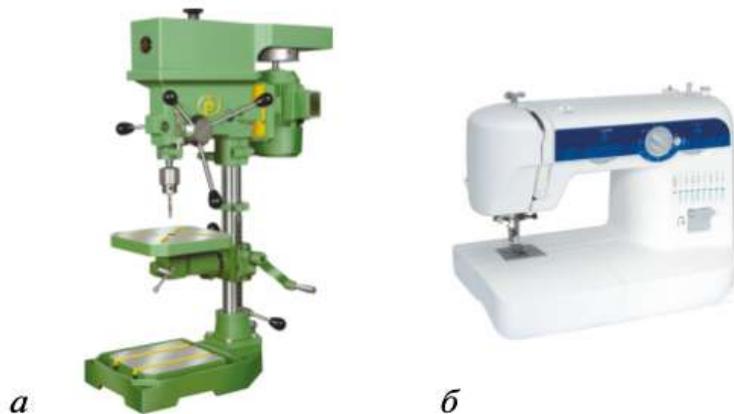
Оборудование: *а* — станок сверлильный; *б* — швейная машина
